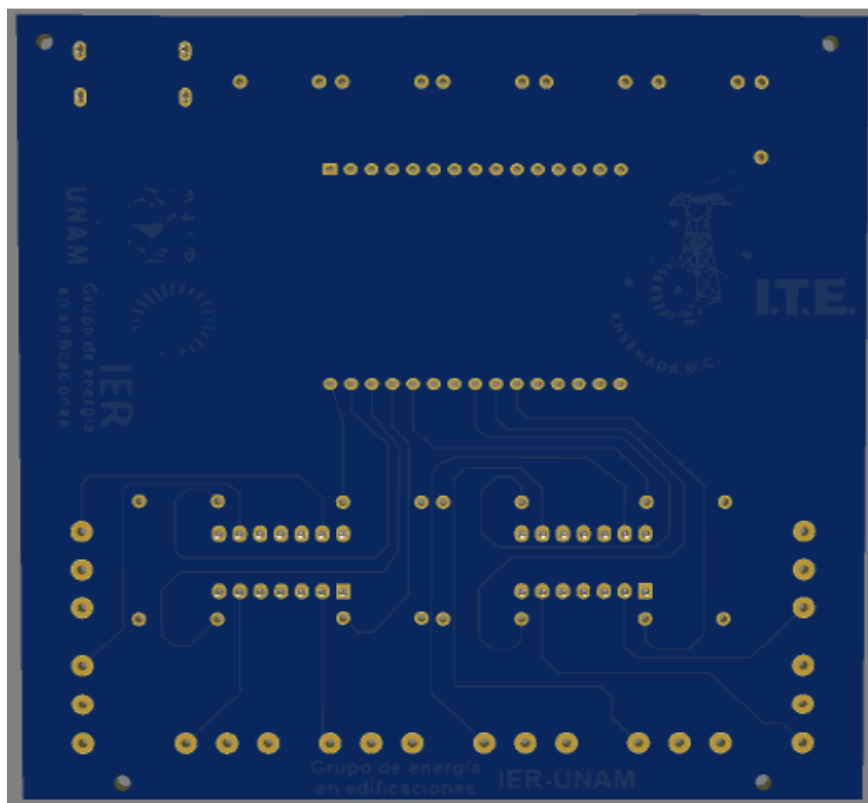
Diseño de PCB del dispositivo H2O (vista inferior)
